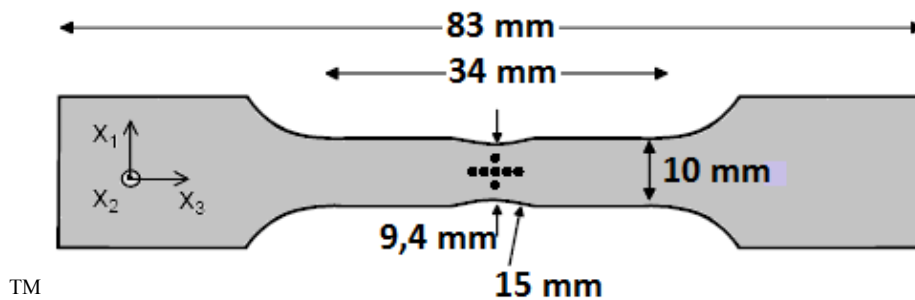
Géométrie des éprouvettes de traction uniaxiale pour machine MTS hydraulique
